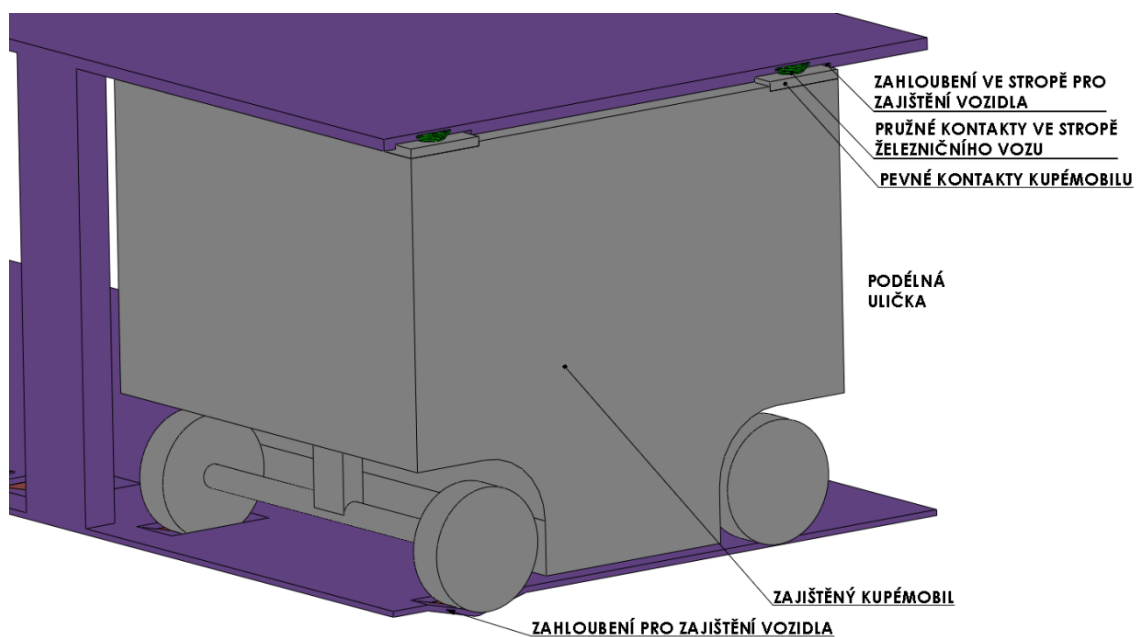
Hrubá stavební struktura - rozložení elektrických kontaktů ve stropě
